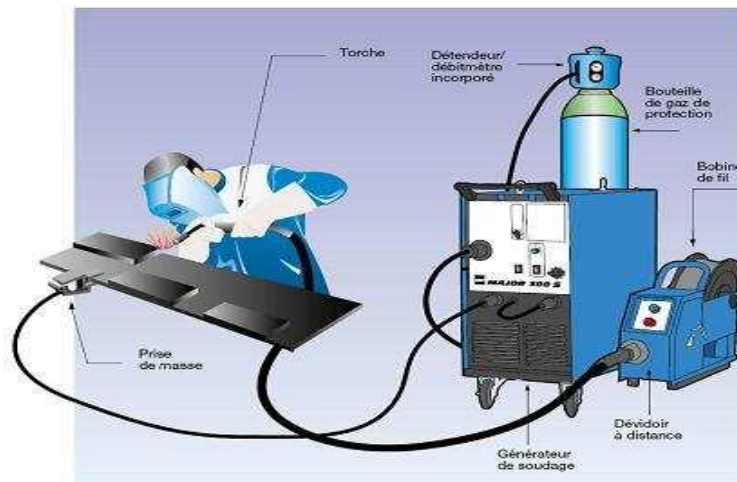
Schéma d'une Opération de soudage MIG/MAG [16].
